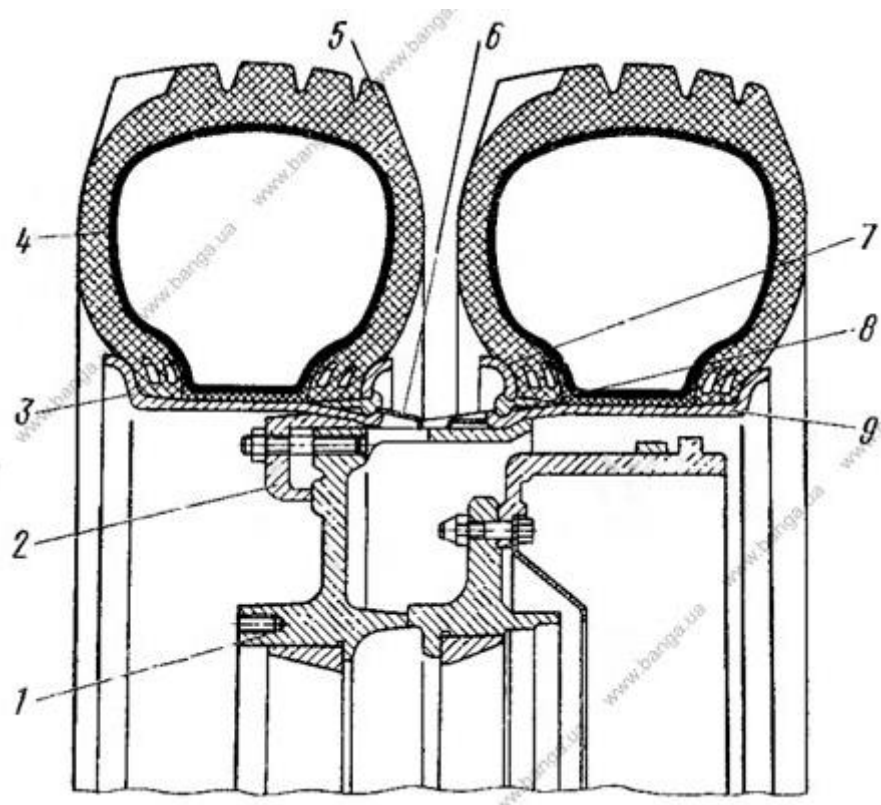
Заднє колесо з гальмівним барабаном у зборі: 1-ступиця; 2-притиск заднього колеса; 3-обід зовнішнього колеса; 4-зовнішня шина; 5 камера; 6-проставкове кільце; 7-бортове кільце; 8-замкове кільце; 9-обід внутрішнього колеса
